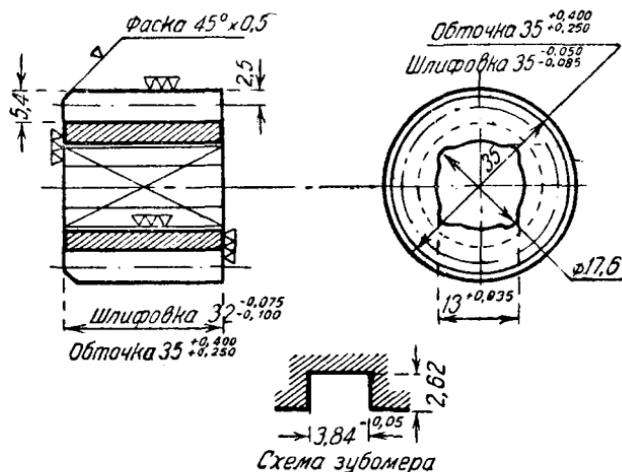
Дет. 222. Внутренняя ведущая шестерня масляного насоса
